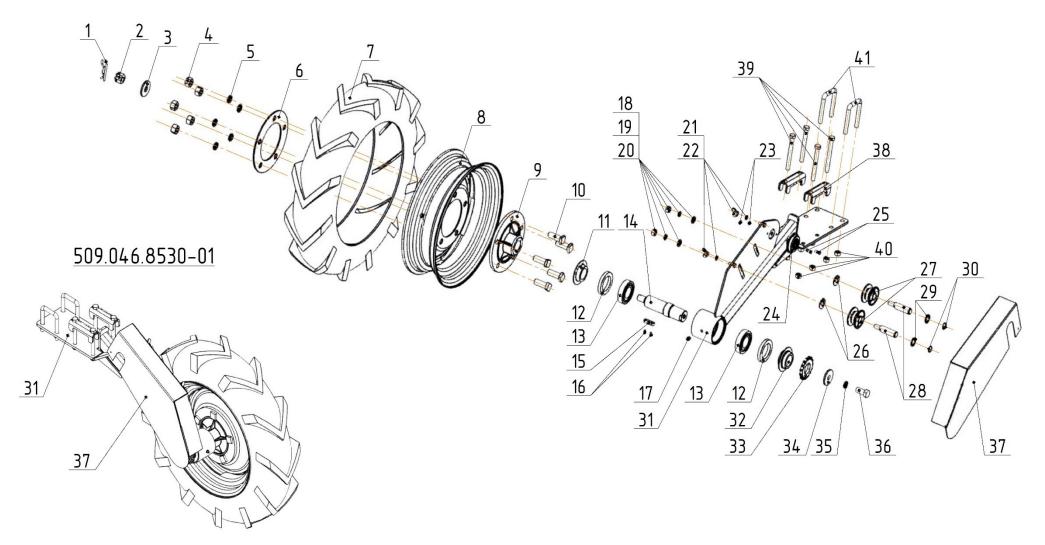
Опорно-приводное колесо 509.046.5030 (правое) Опорно-приводное колесо 509.046.5030-01 (левое)
